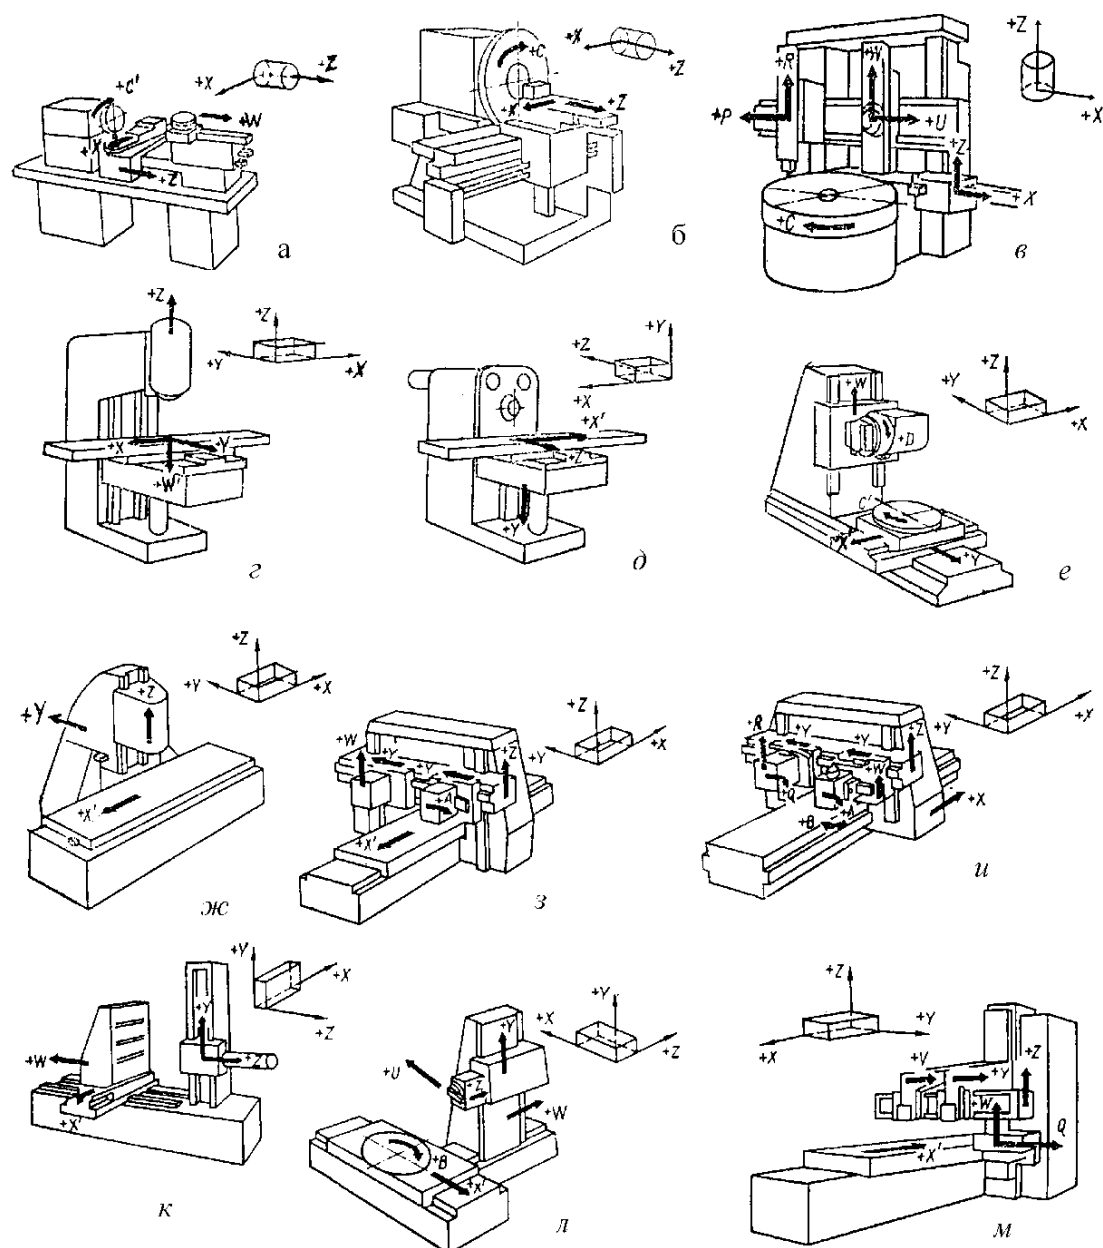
Обозначение осей и направлений перемещений станков:
